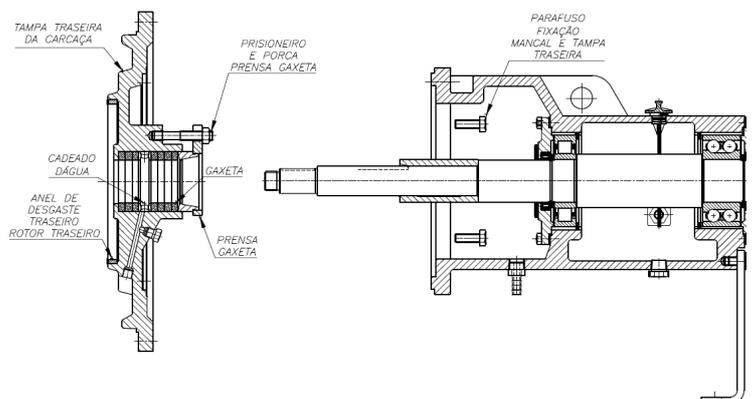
Soltando parafusos mancal-tampa traseira e removendo a tampa
